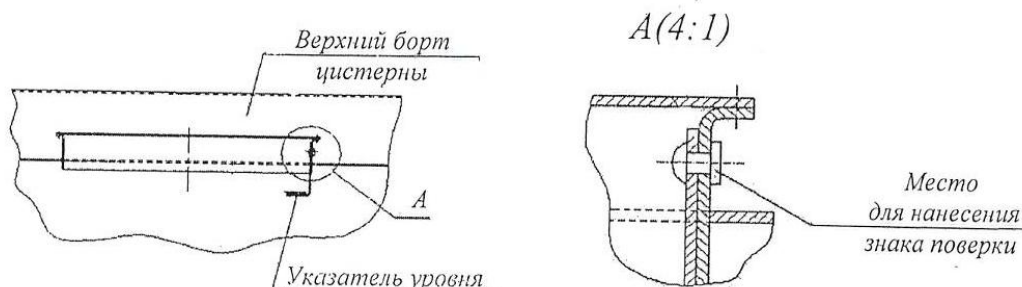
Схема пломбировки и обозначение места для нанесения знака поверки
